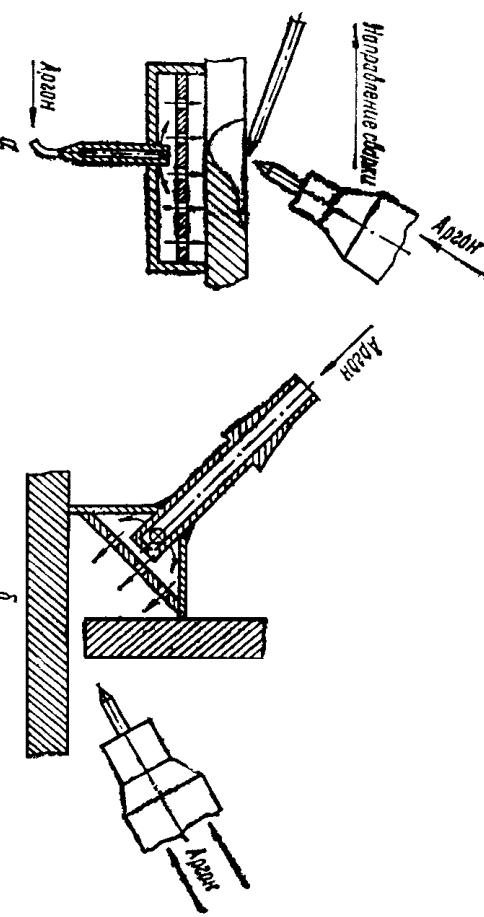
Камера для защиты обратной стороны шва стыковых (а) и тавровых (б) соединений.
